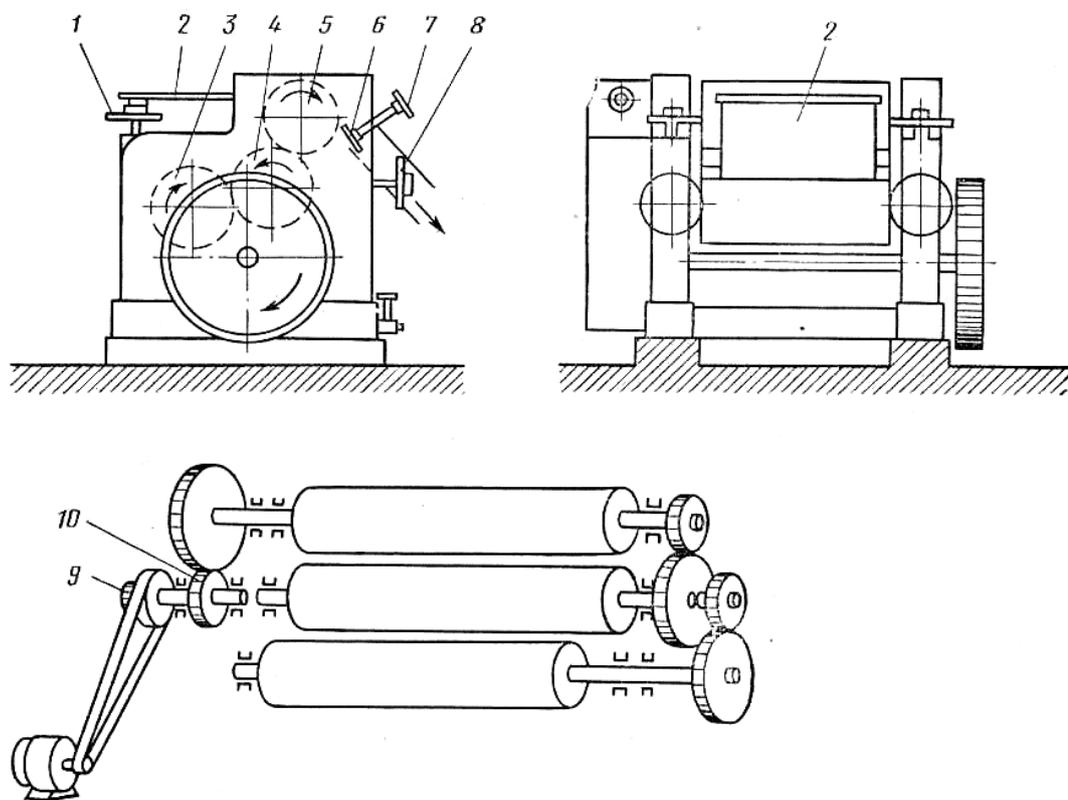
Вальцовка: 1,8 – регулировочные винты; 2 – загрузочный бункер; 3,4,5 – вальцы; 6 – нож; 7 – нажимные винты; 9 – привод; 10 – цилиндрический редуктор
